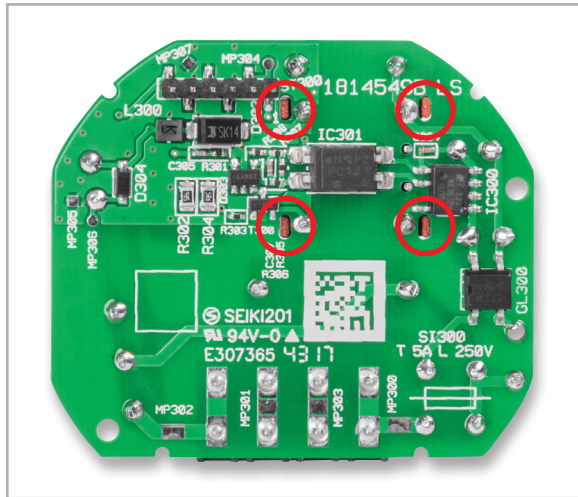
dass die vier Gehäusezapfen komplett in die zugehörigen Platinschlitzlötlücken eingeführt sind.
